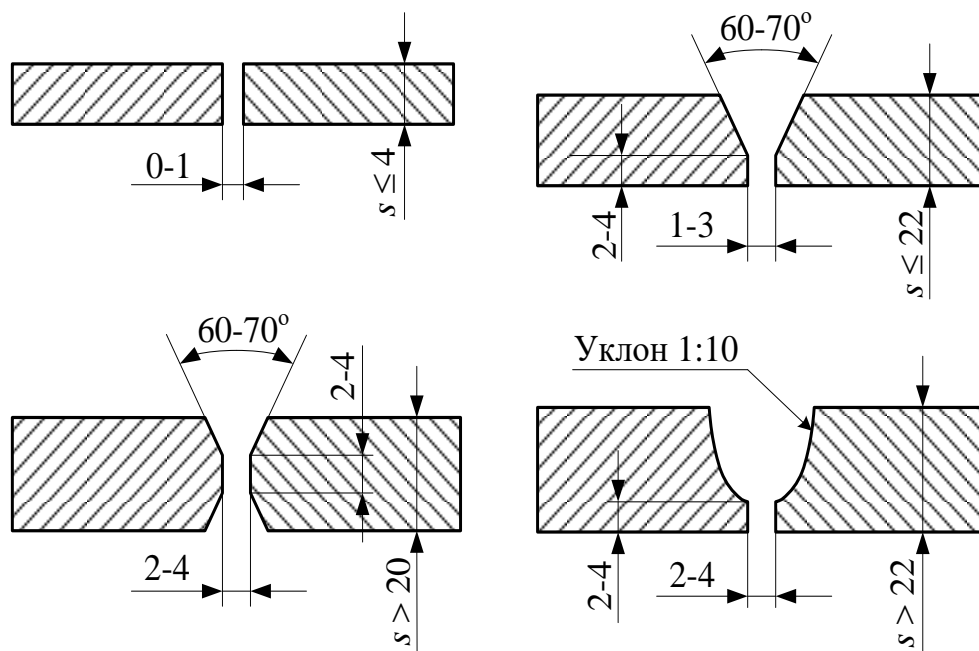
Підготовка кромки для ручного дугового зварювання в залежності від товщини листа
